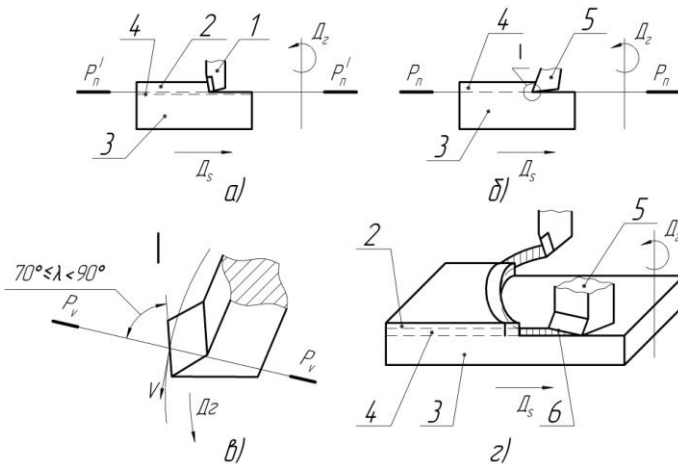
Схема скользящего торцевого фрезерования при больших глубинах резания
